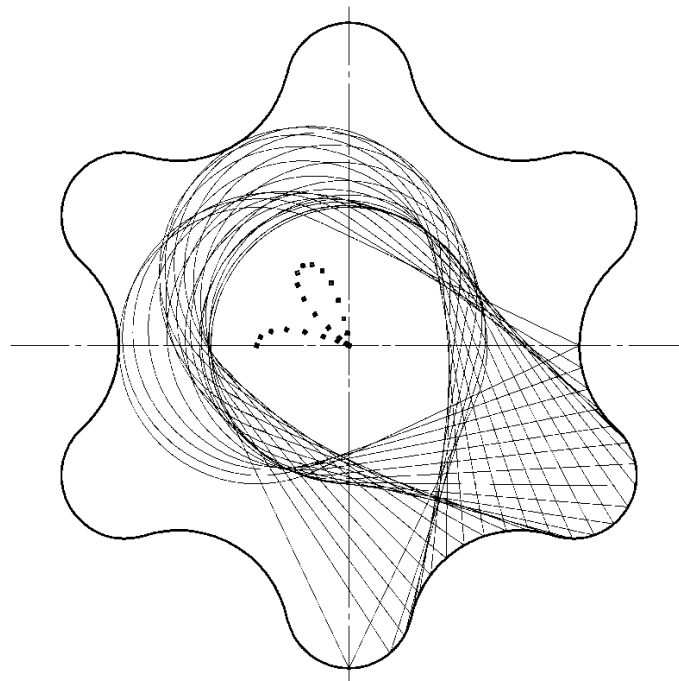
Теоретический процесс обработки отверстий типа TORX
